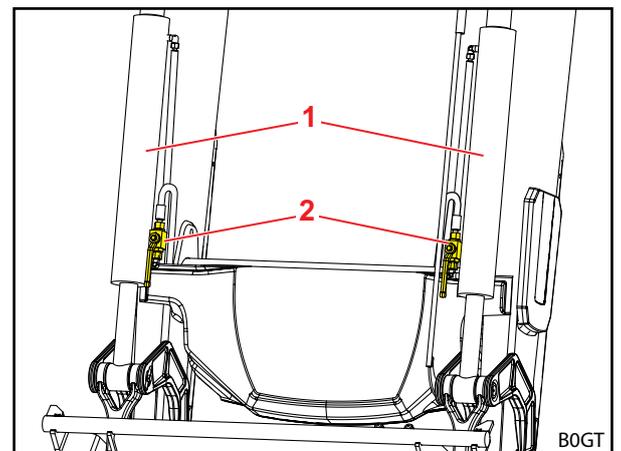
Absperrhähne an den Werkzeug-Zylindern
